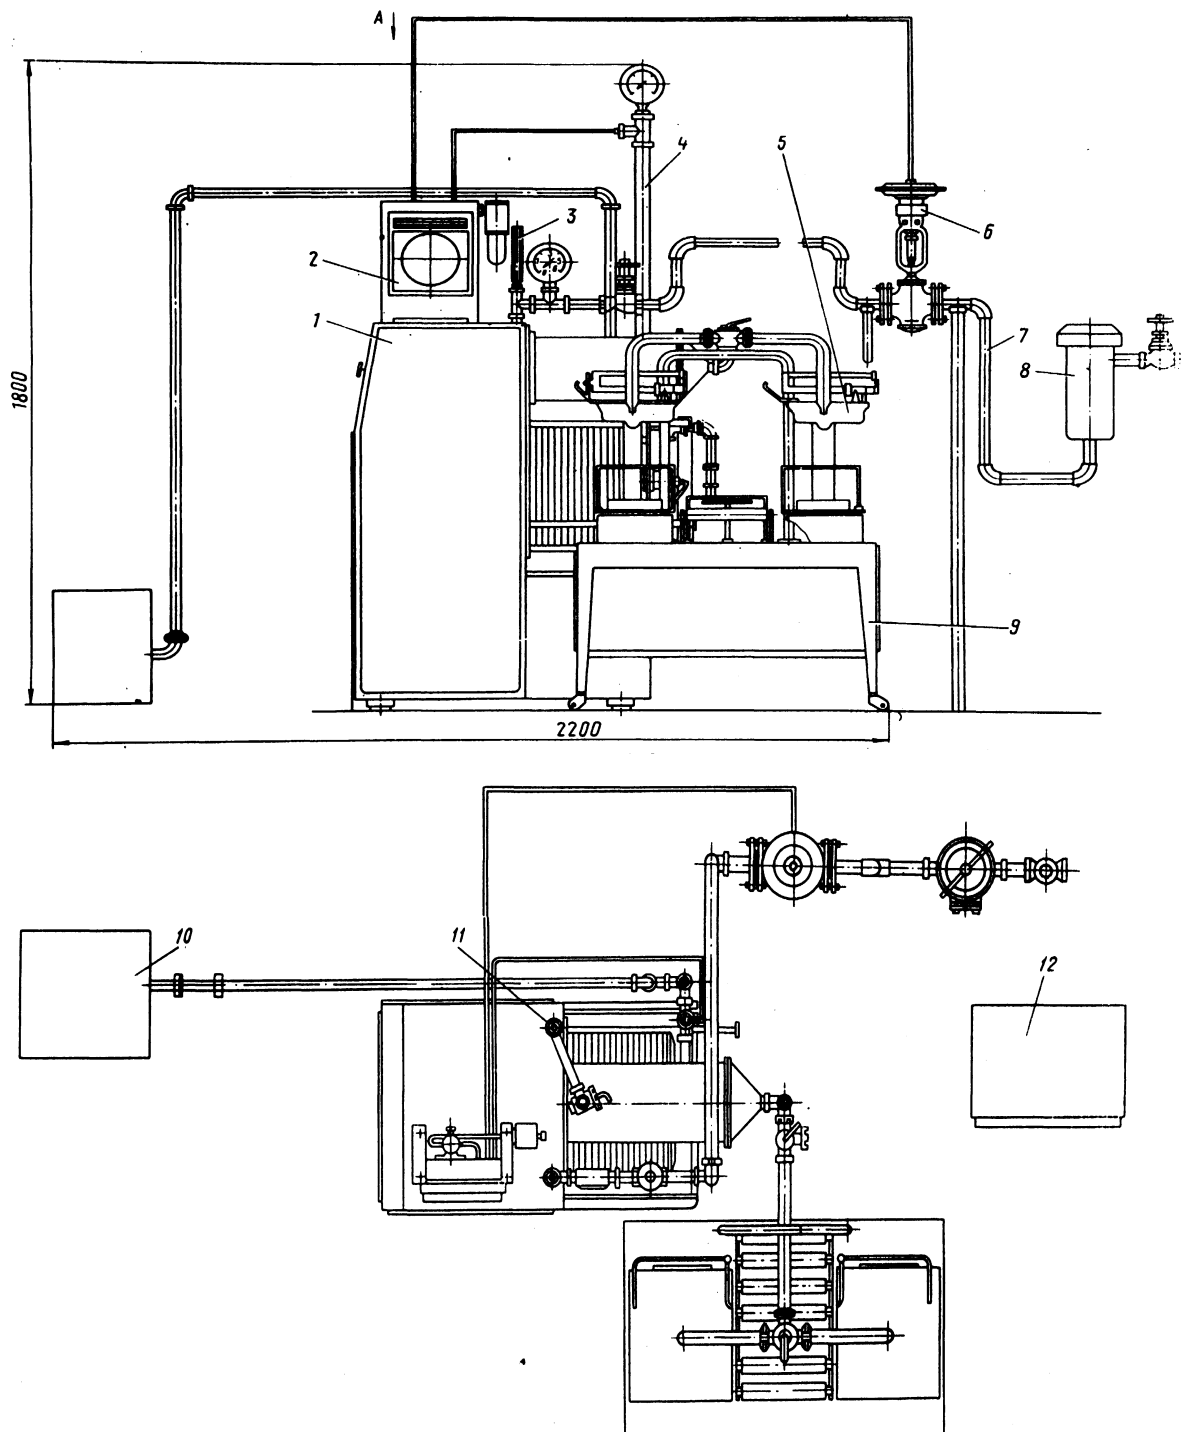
Загальний вид установки марки РЗ-ОУА:
